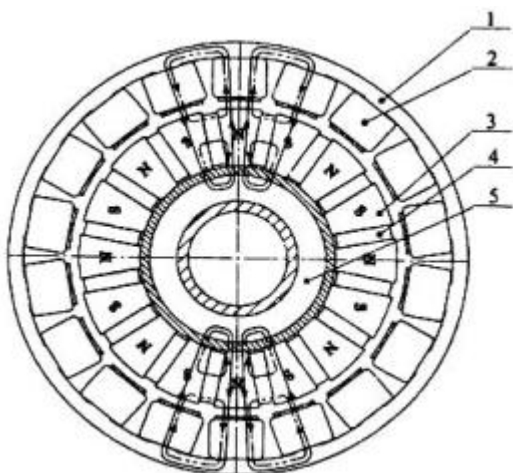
Редукторный электродвигатель с дробными однозубцовыми обмотками $q < 1$
